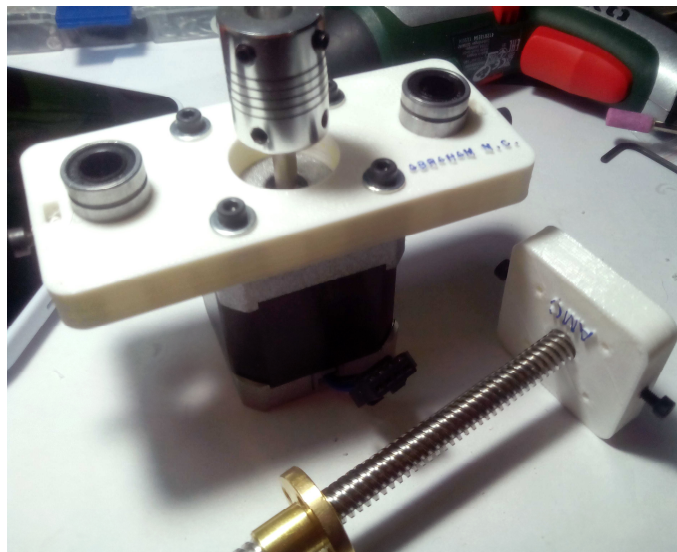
Soportes motor (derecha) y husillo (izquierda)
